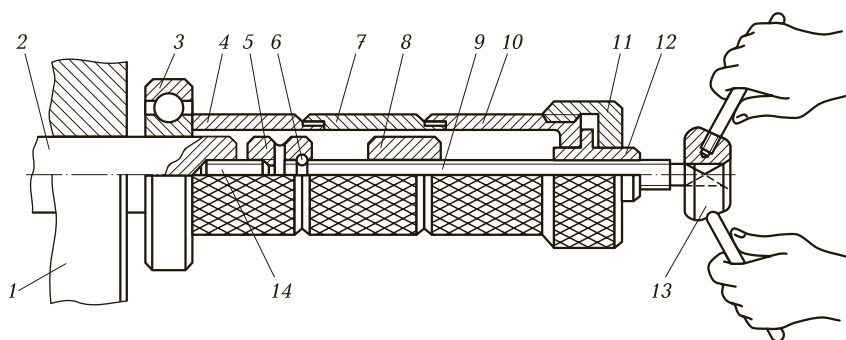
Приспособление для напрессовывания подшипников на вал:
